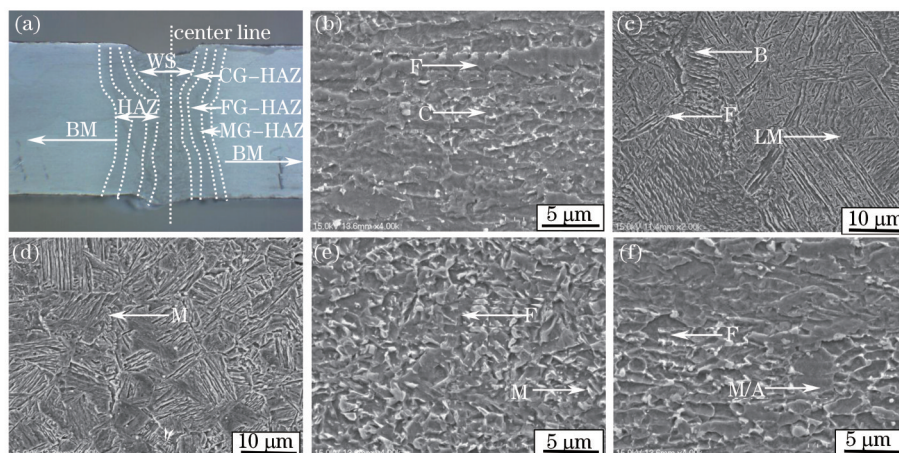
焊接接头的宏观及微观组织(热输入 226 J/mm²)。 (a) 宏观形貌; (b) 母材; (c) 焊缝; (d) 粗晶区; (e) 细晶区; (f) 混晶区
